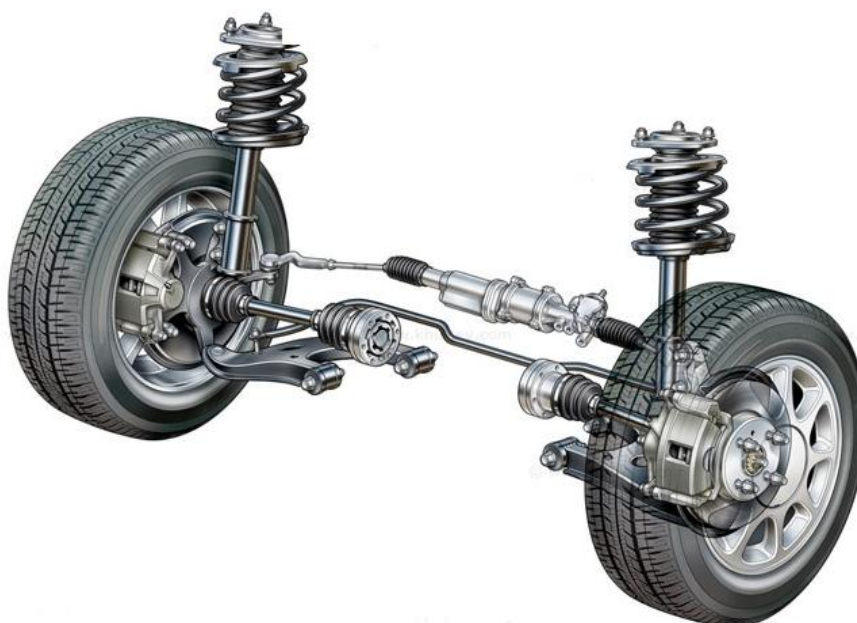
Čtyřprvková přední náprava Audi A4 [3]
